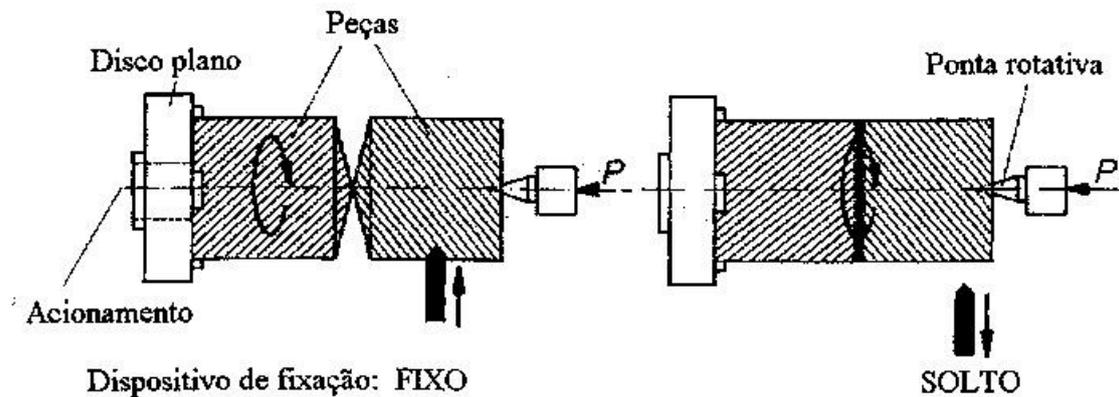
Soldagem por atrito rotacional (MICHAELI et al.,1995)
